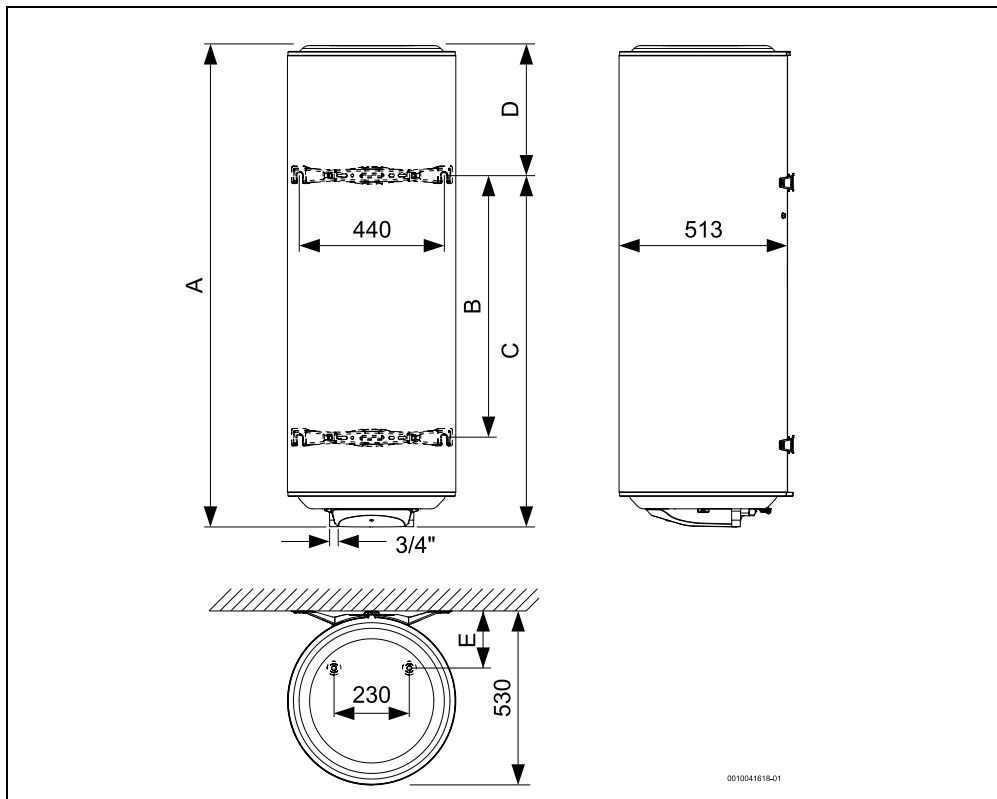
Dimensões em mm (montagem mural, instalação vertical)
